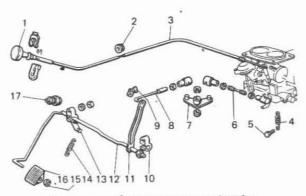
Transmisión de mando del carburador 2107-1107010:
